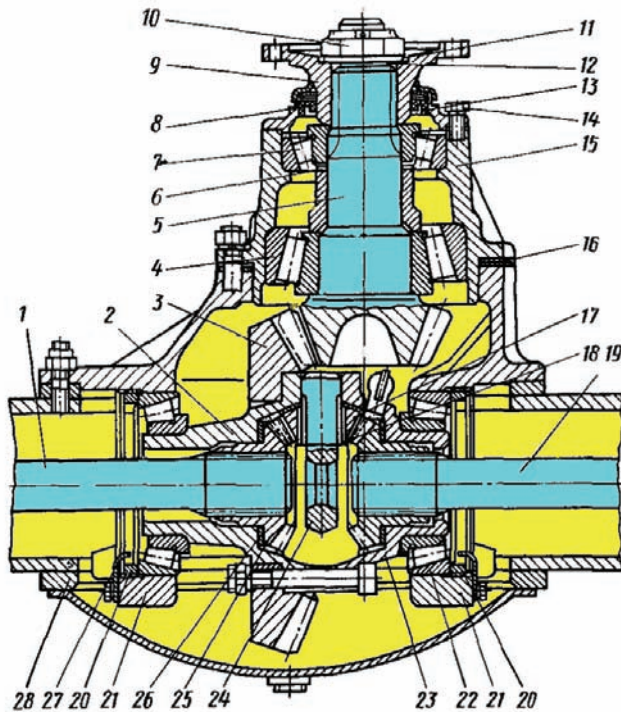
Центральный редуктор заднего моста: 1, 19 — полуоси; 2, 23 — чашки дифференциала; 3 — ведомая шестерня; 4, 7, 22 — подшипники; 5 — ведущая шестерня; 6, 16 — регулировочные прокладки; 8 — сальник; 9 — фланец; 10 — гайка; 11 — шайба; 12 — уплотнительное кольцо; 13 — крышка; 14 — болт; 15 — корпус подшипников; 17 — сателлит; 18 — упорное кольцо; 20 — гайка подшипника дифференциала; 21 — крышка подшипника; 24 — крестовина; 25 — полуосевая шестерня; 26 — шайба; 27 — стопор гайки подшипника; 28 — картер моста
